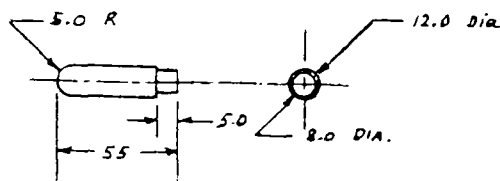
Couper la tige de bois aux dimensions indiquées. Réduire le diamètre à une extrémité et arrondir l'autre extrémité.
